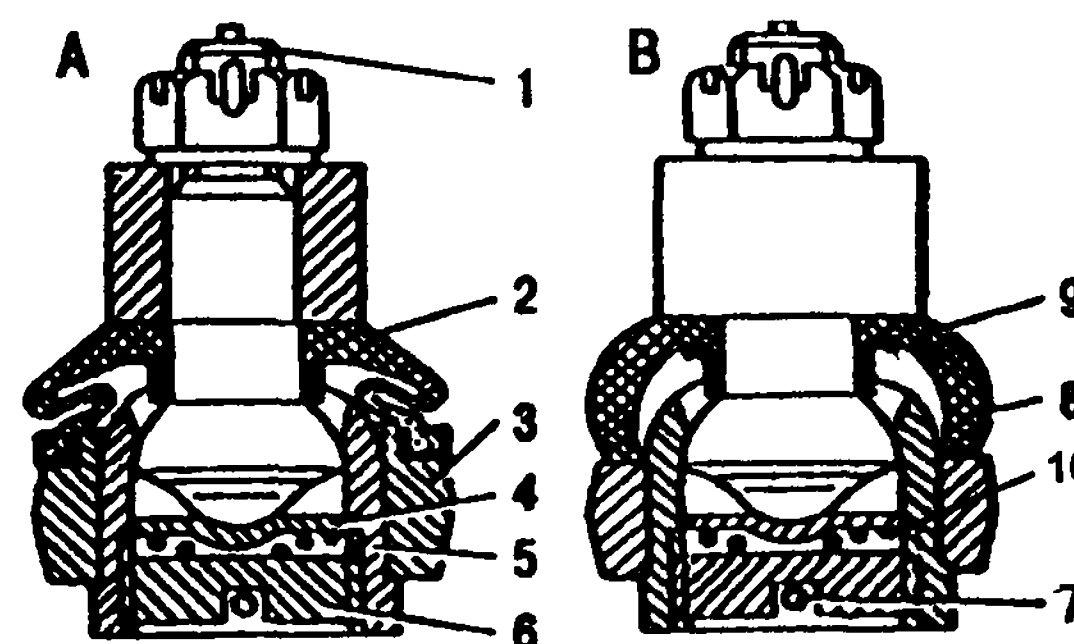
Шаровые шарниры тяг рулевой трапеции: 1 - шаровый палец; 2 - резиновый уплотнитель; 3 - тяга; 4 - опорная пята; 5 - корпус шарнира; 6 - заглушка; 7 - шплинт; 8 - уплотнитель тяги сошки и маятникового рычага; 9 - распорная втулка; 10 - пружина; А - шарнир наконечника и средней тяги рулевой трапеции; В - шарнир тяги сошки
